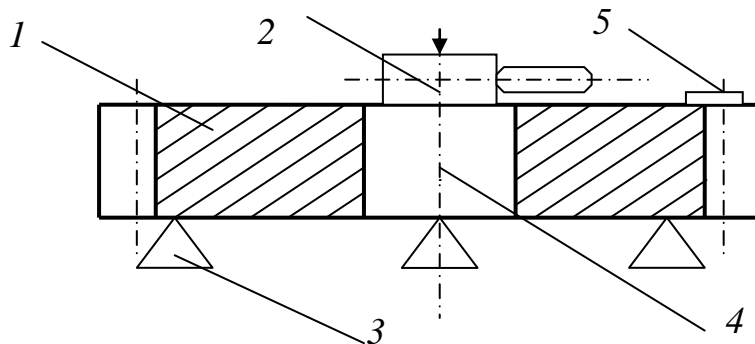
Схема установки крупногабаритного зубчастого колеса:
